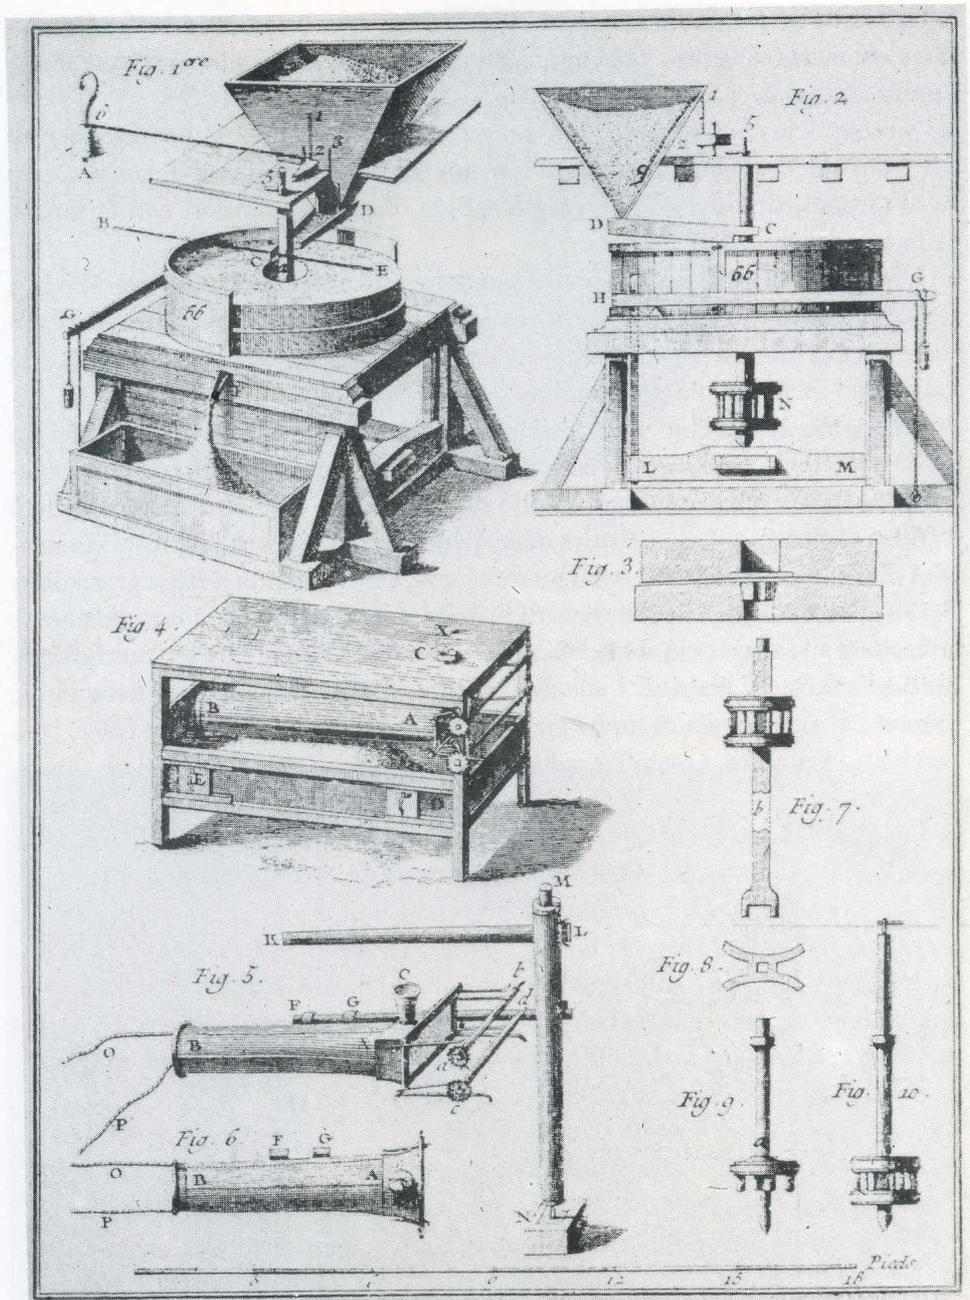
Schema di impianto molitorio completo di buratto (n. 4-5-6).
